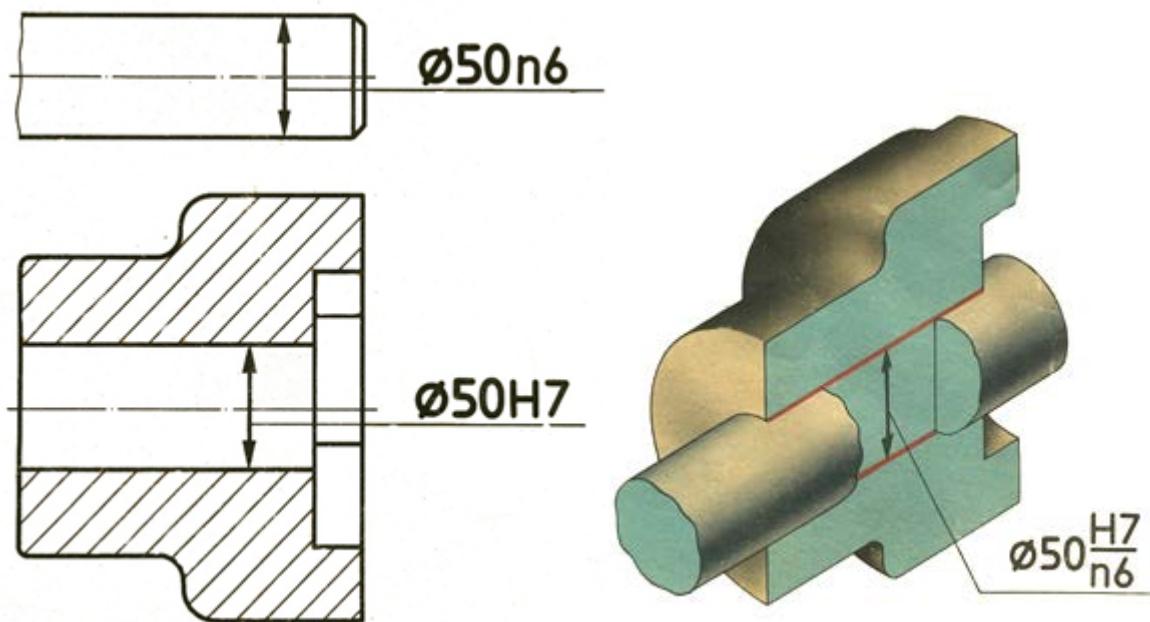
Неподвижная часть кулачковой муфты с валом, точность высокая, резкие нагрузки, разборка крайне редка
